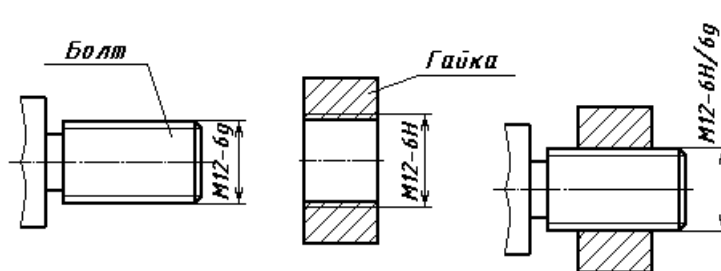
Обозначение метрической резьбы на чертежах
